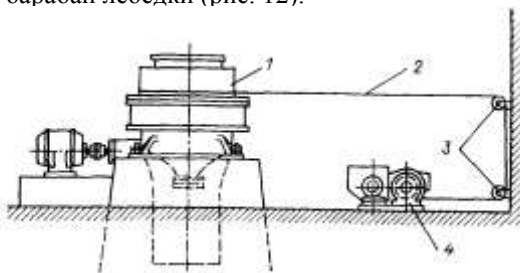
Изменение ширины разгрузочной щели конусной дробилки с пологим конусом: 1 – кожух регулирующего кольца; 2 – трос; 3 – направляющие блоки; 4 – электролебедка.
